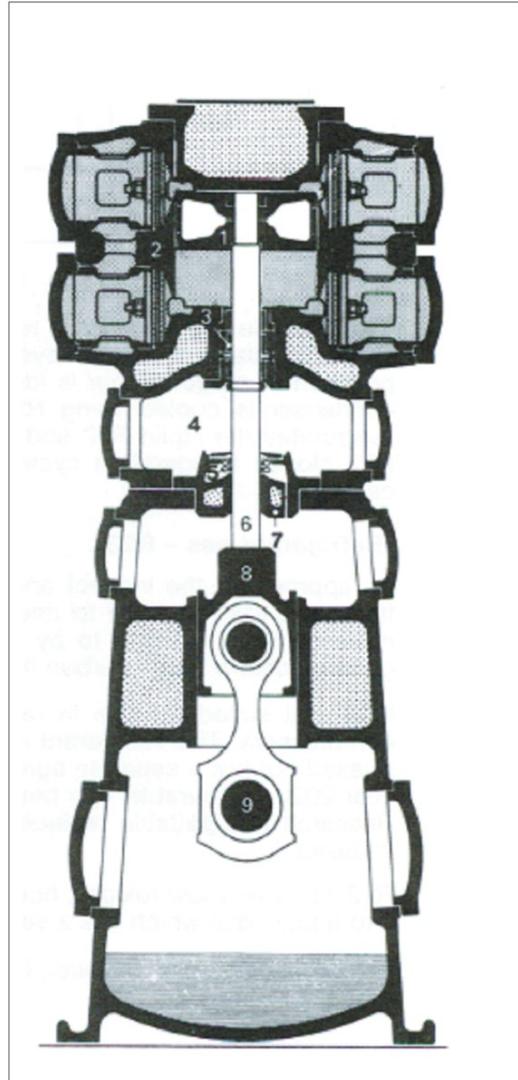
Ölfreier Kompressor von Sulzer
